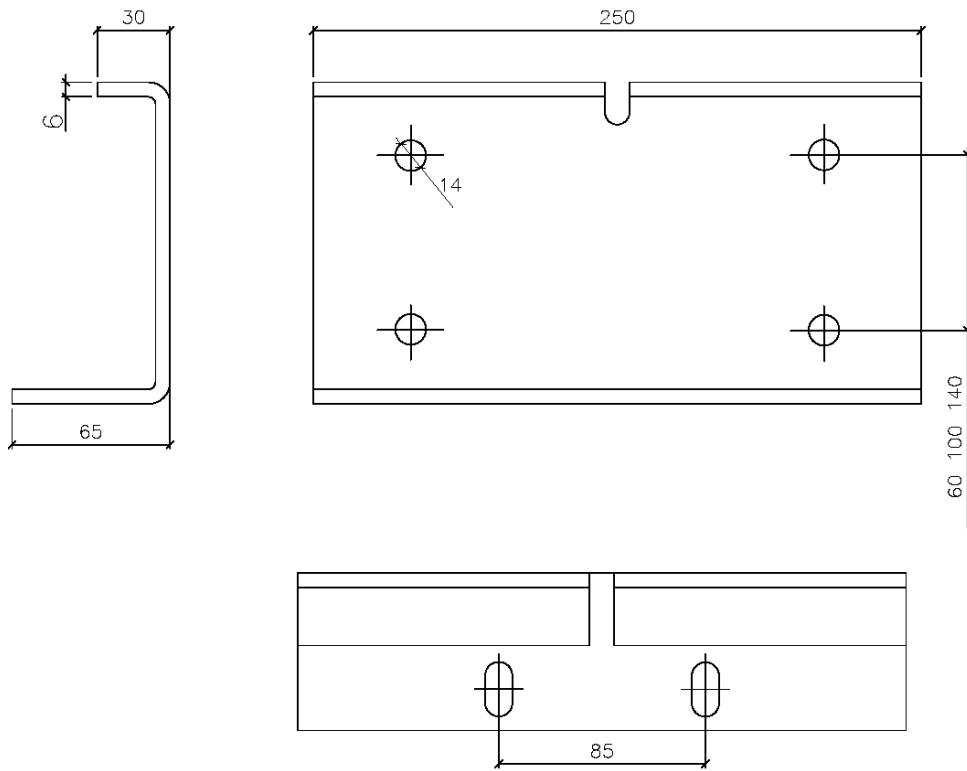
ESQUEMA DE MONTAJE VIGA TIPO MVV
